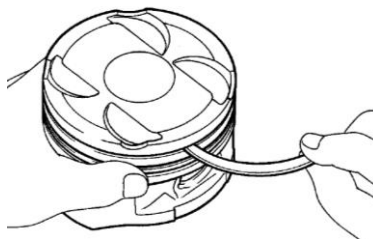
Снятие и установка поршневых колец с помощью приспособления
